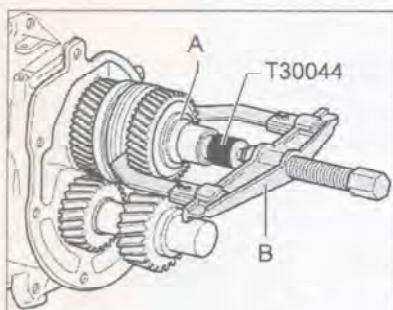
Снимите шестернию 5-й передачи с внутренней обоймой подшипника (A) с первичного вала с помощью съемника Kukko 20/10 (B).
